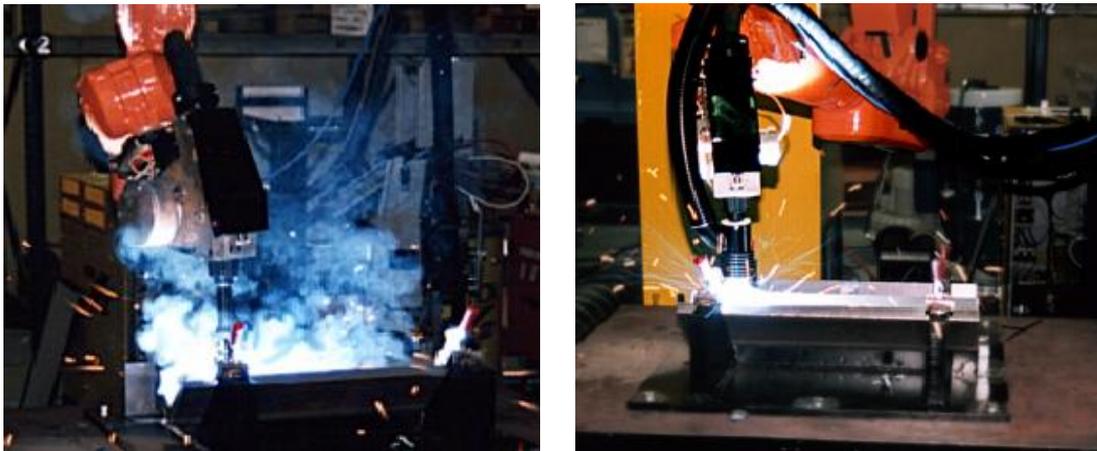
Extracción localizada de alto vacío en robots de soldadura
